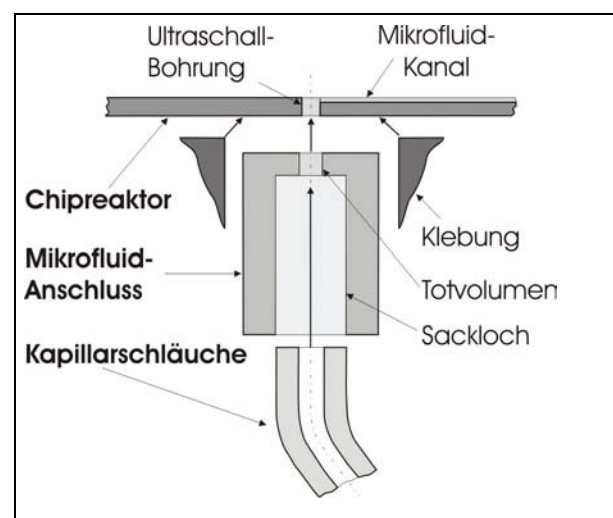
Fluidische Anschluss technik (Explosionszeichnung)
